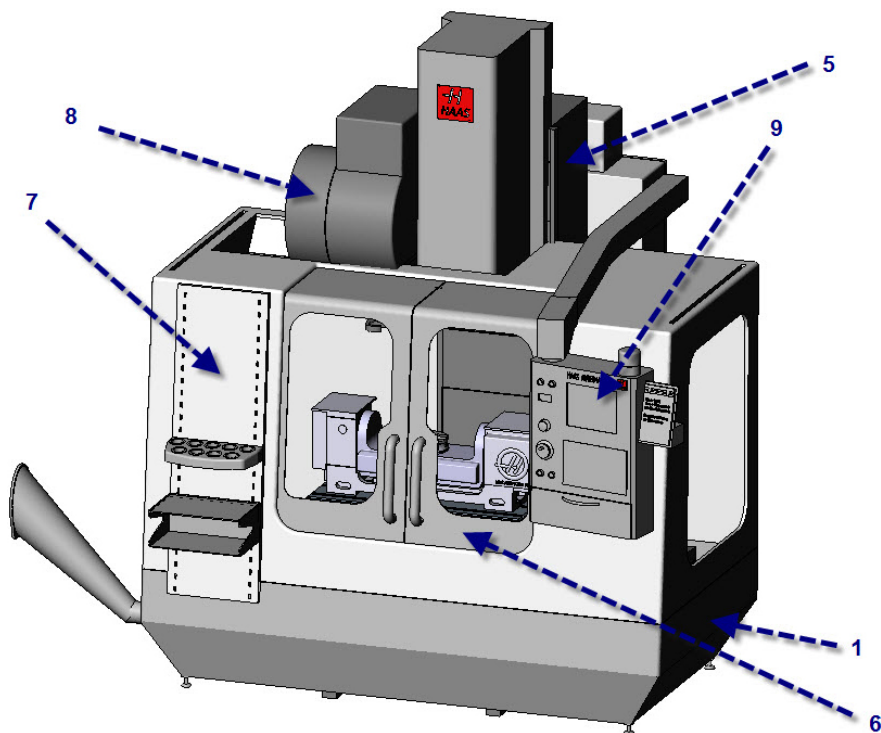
Корпус вертикально-фрезерного станка с ЧПУ
